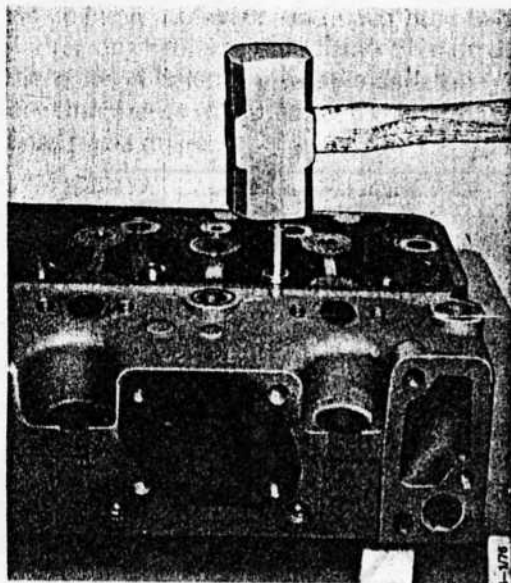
Se saca el anillo de asiento de válvula con la válvula soldada
